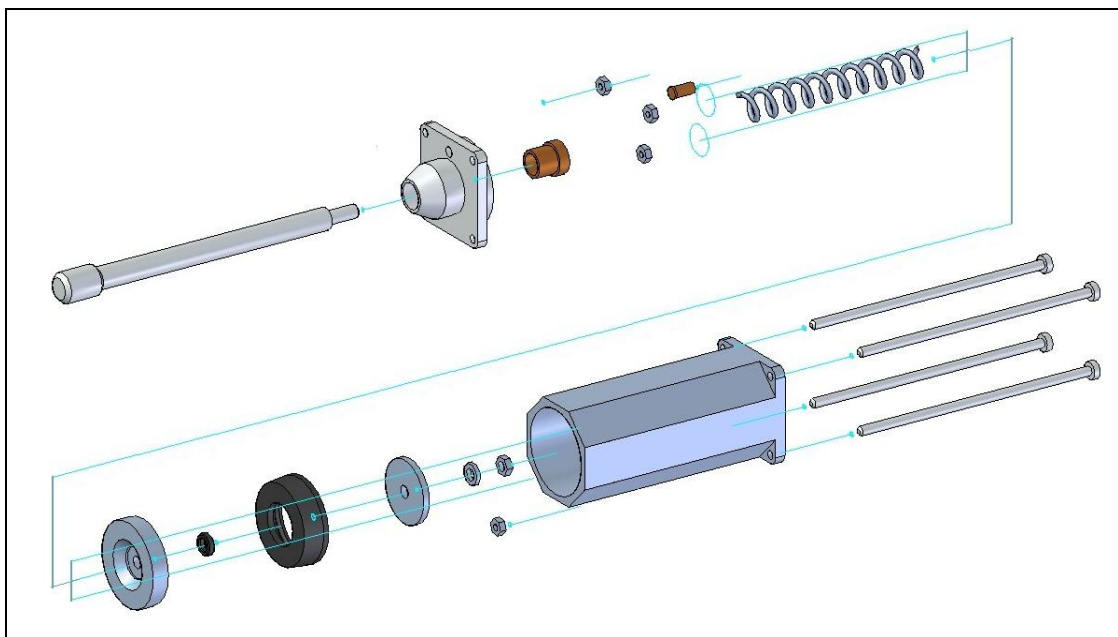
Cilindro de simple efecto con retorno por muelle – Explosionado
